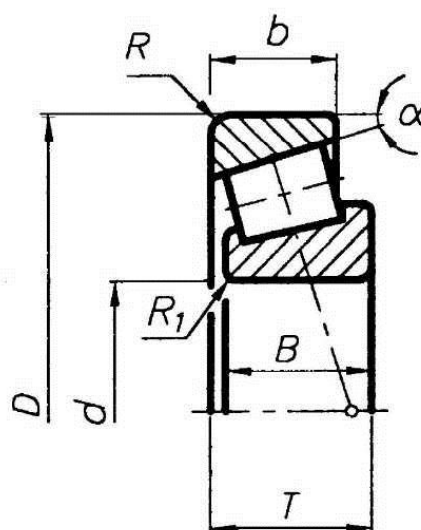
Габаритные размеры роликовых конических однорядных подшипников
